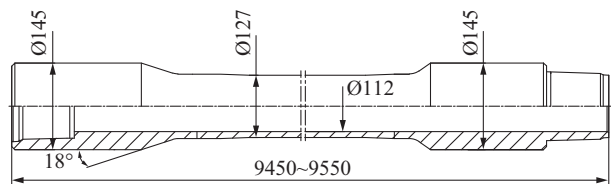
$\varnothing 127$ mm 钻杆轮廓尺寸
